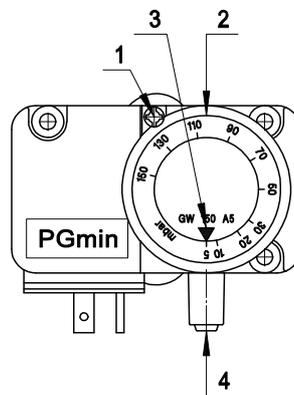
1-Винт заглушка 2-Регулировочная гайка 3-Указатель регулировки 4-Разъем для измерения давления
